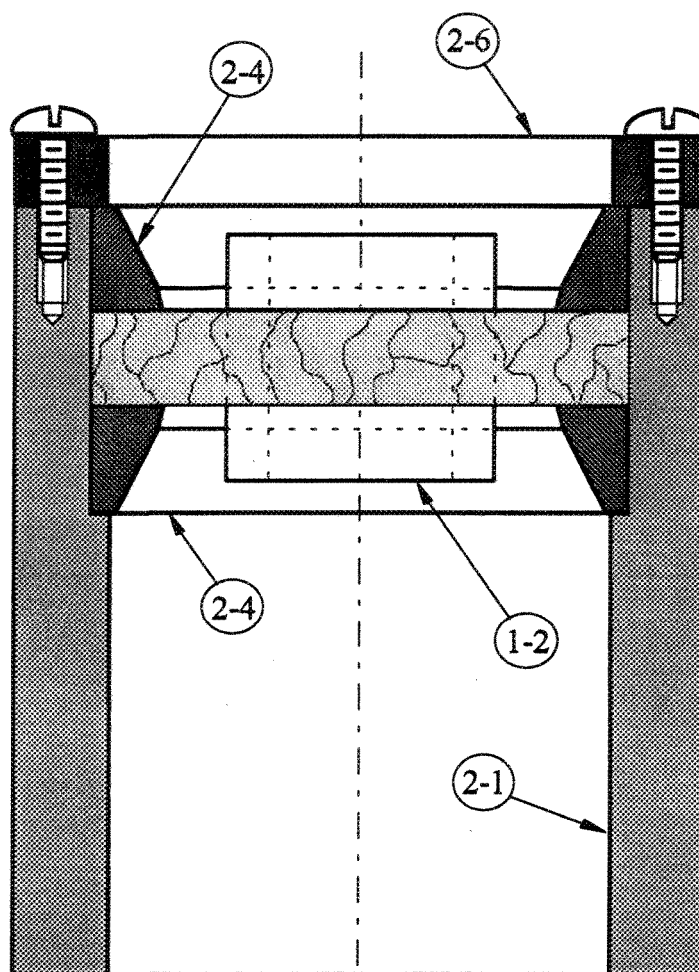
Adaptateur guide fixé à la cellule de charge de la presse (les dimensions sont exprimées en mm).
